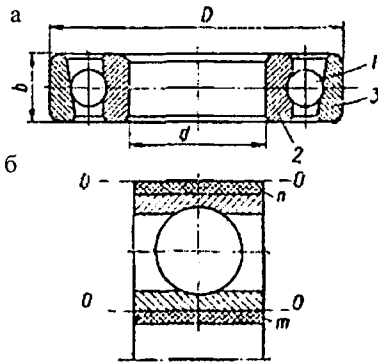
Загальний вигляд (а) і схема (б) полів допусків зовнішнього (п) і внутрішнього (м) кілець підшипника котіння.
